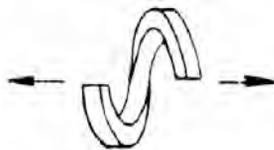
Empaquetadura de la caja de empaquetadura: correcto
